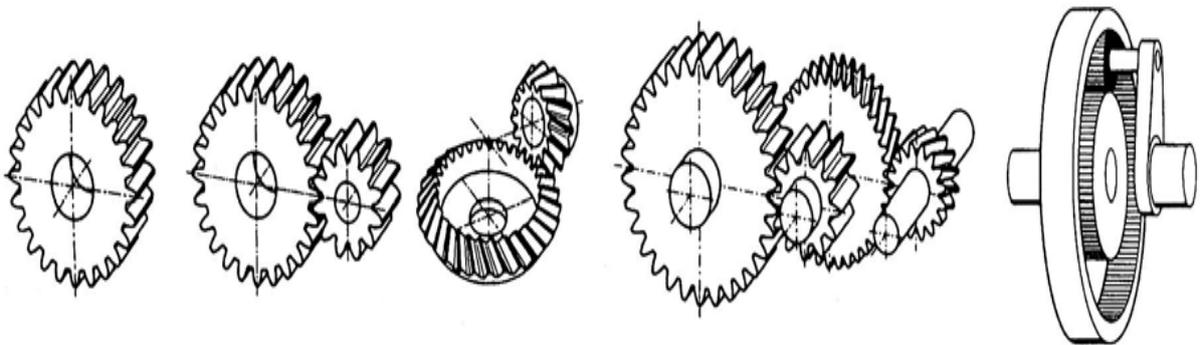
Roues d'engrenage, engrenage, train d'engrenages, train planétaire [22]
